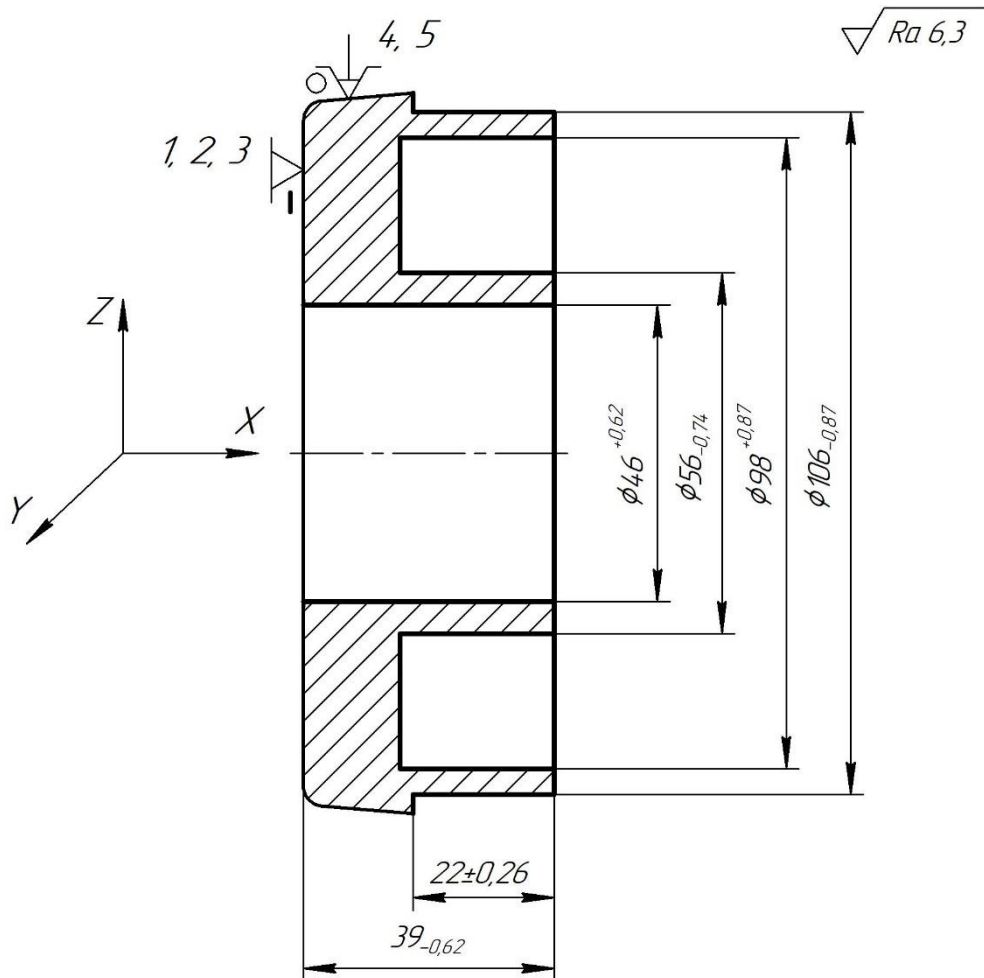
Схема базування й закріплення заготовки на операції 025, установ А
